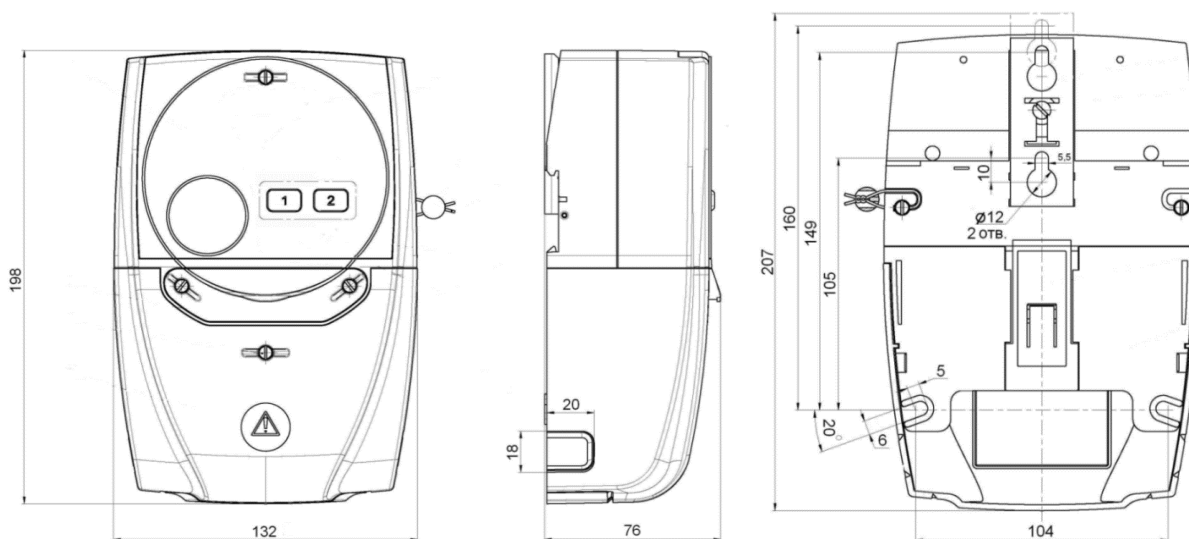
Габаритные и установочные размеры коммуникатора
